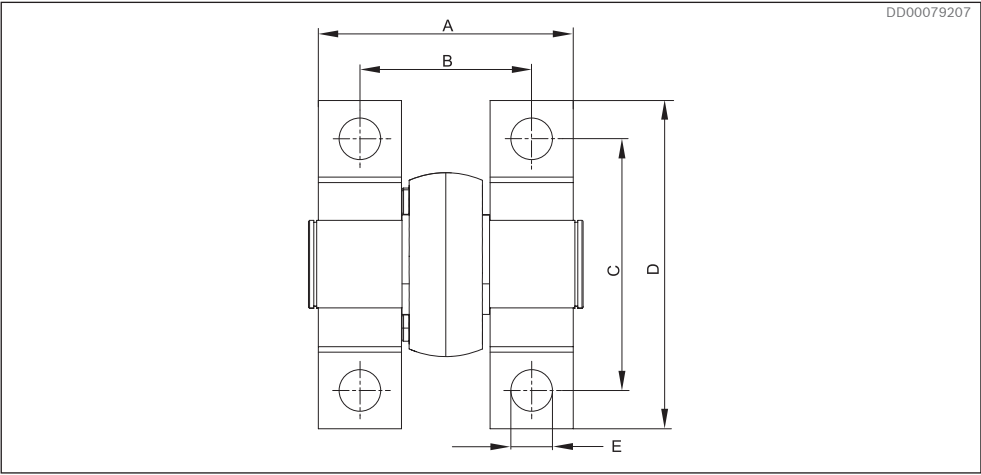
Расположение отверстий для шарнирного соединения и гидравлического цилиндра при использовании DTCBM 1600 – DTCBM 4000
